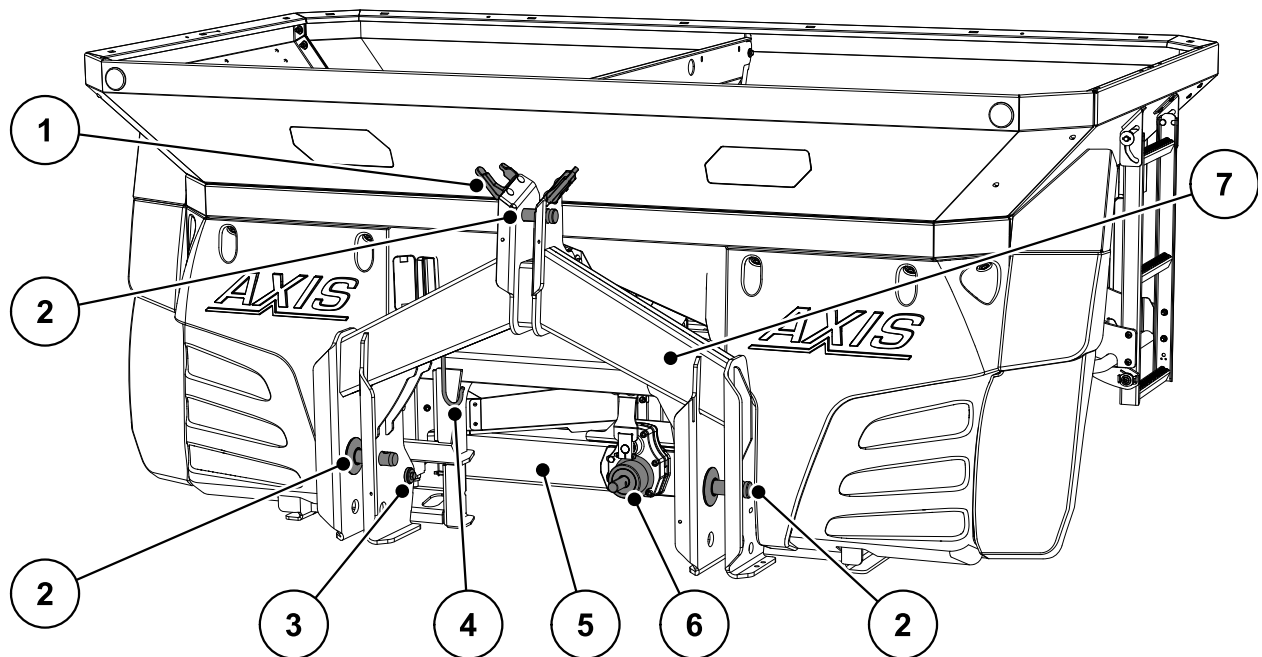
Komponentgruppöversikt AXIS 50.1, - framsida
